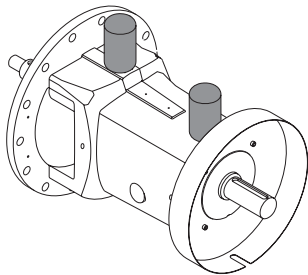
Корпус подшипников с ниппелями для консистентной смазки
